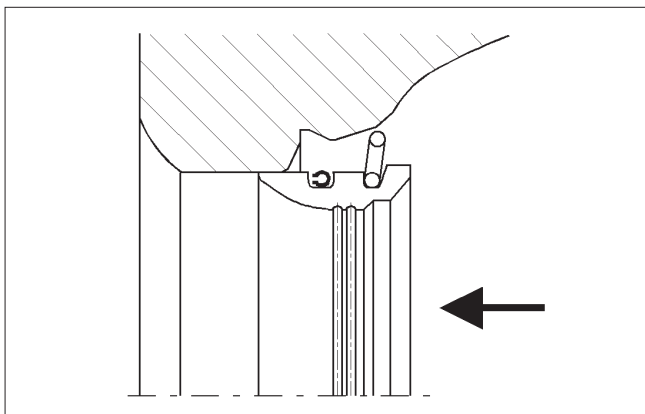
Drücken Sie die Federwinkel gegen die Kontrollfläche
